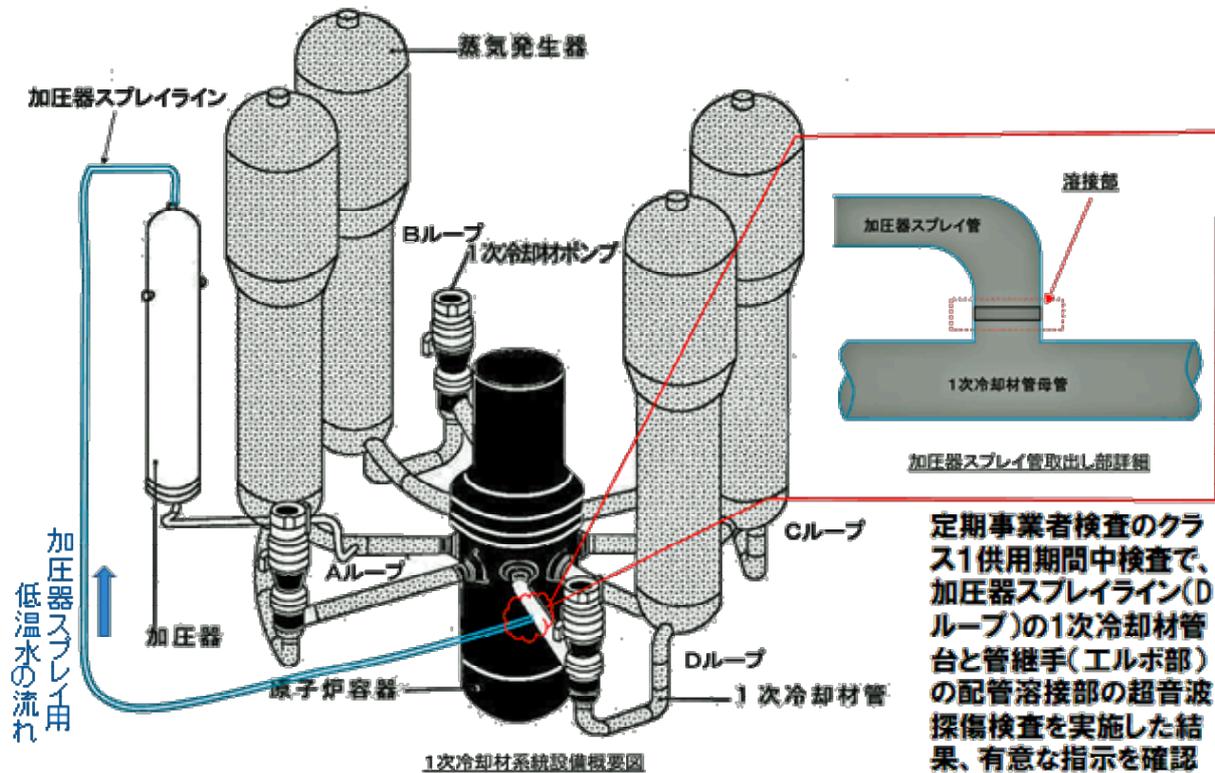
大飯3号機加圧器スプレイライン配管溶接部に生じた深さ4.6mm(肉厚の1/3)、長さ67mmのひび割れの状況
